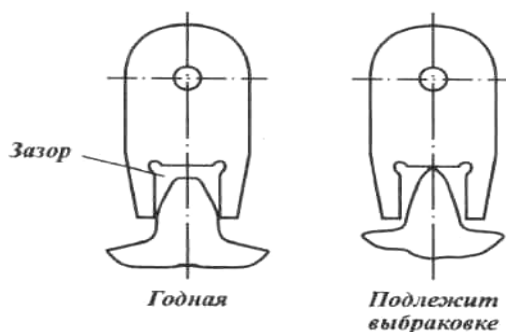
Схема контроля годности цилиндрических шестерен контрольной скобой
